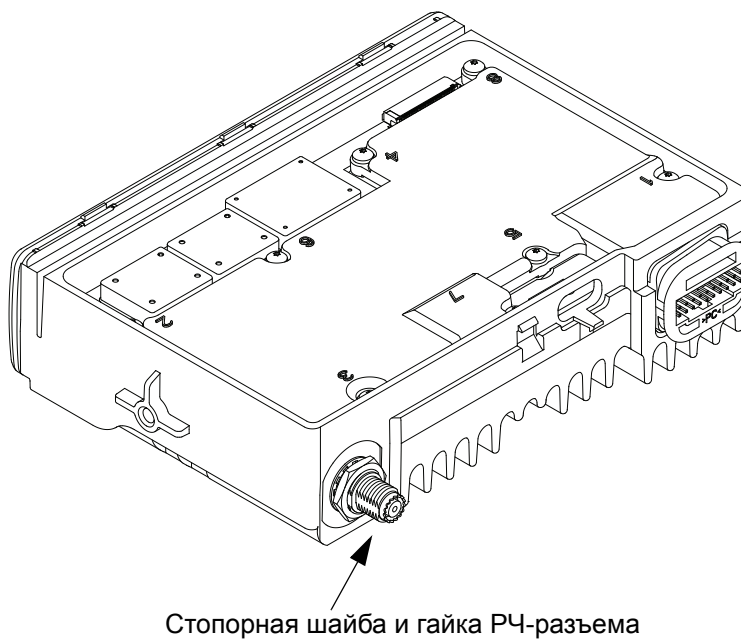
Окончательный момент затягивания гайки РЧ-разъема
